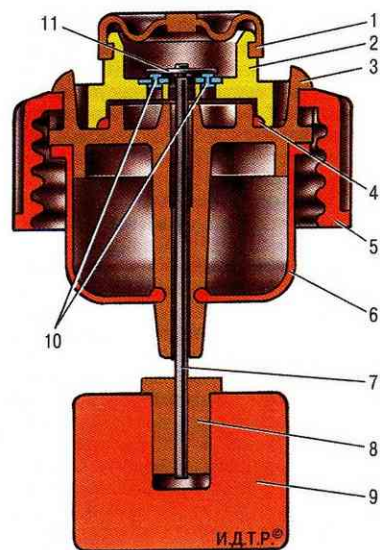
Датчик аварийного уровня тормозной жидкости: 1 - защитный колпачок; 2 - корпус датчика; 3 - основание датчика; 4 - уплотнительное кольцо; 5 - зажимное кольцо; 6 - отражатель; 7 - толкатель; 8 - втулка; 9 - поплавок; 10 - неподвижные контакты; 11 - подвижный контакт
